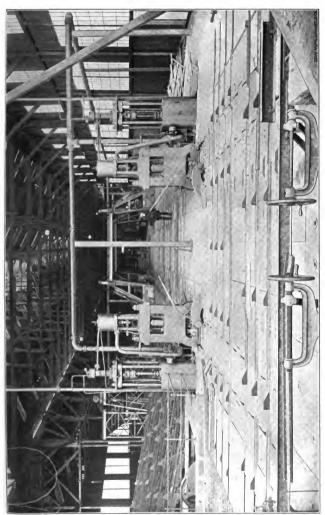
Erstes Walzgerüst der Fertigstrafse.
